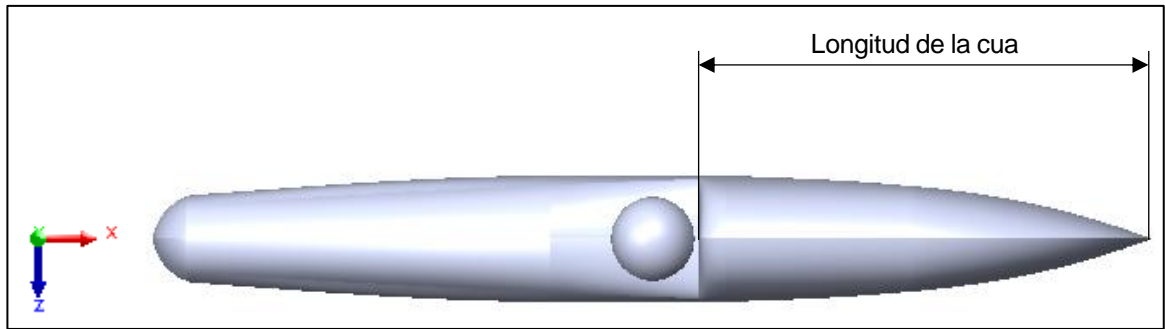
Vista en planta d'una cadira de parapent amb cua.
